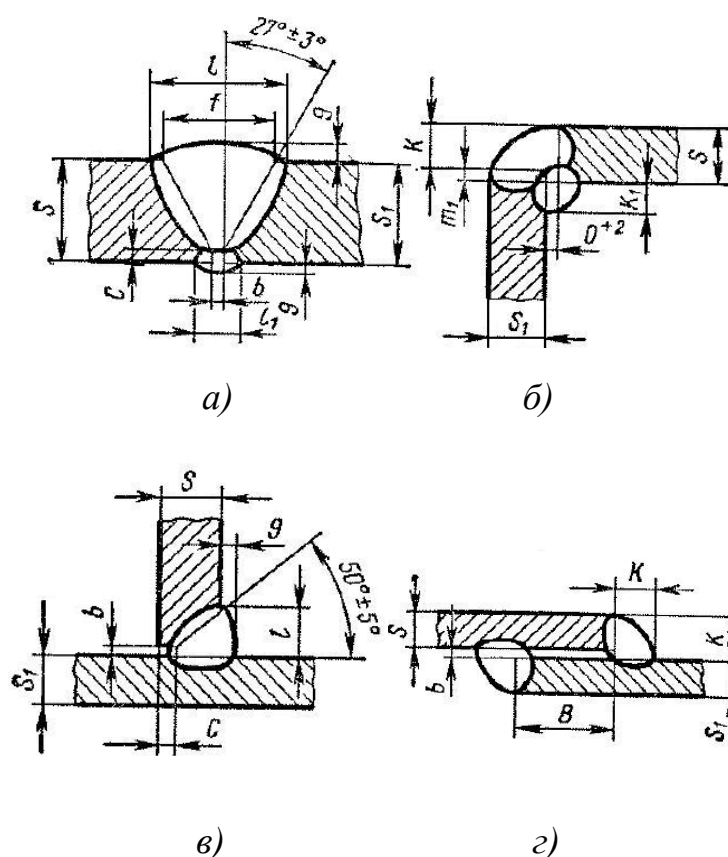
Виды сварных соединений: а) стыковой шов; б) угловой шов, в) тавровый шов г) шов внахлестку
